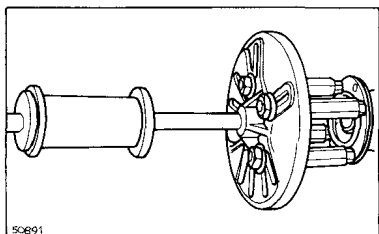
Снятие ступицы колеса со шлицевой части корпуса ШРУС с помощью съемника
